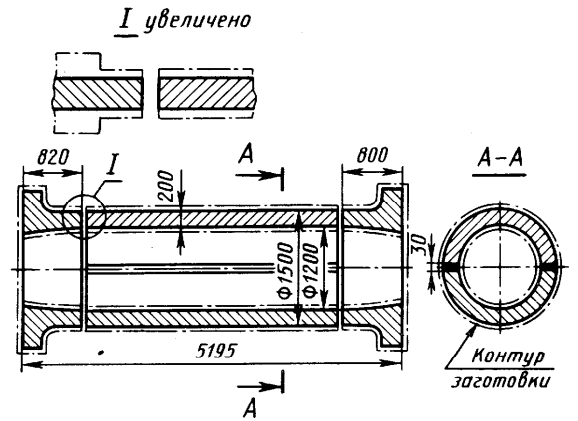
Вал гидротурбины со сварными фланцами и обечайкой
